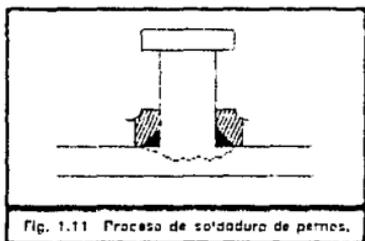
Proceso de soldadura de pernos.
